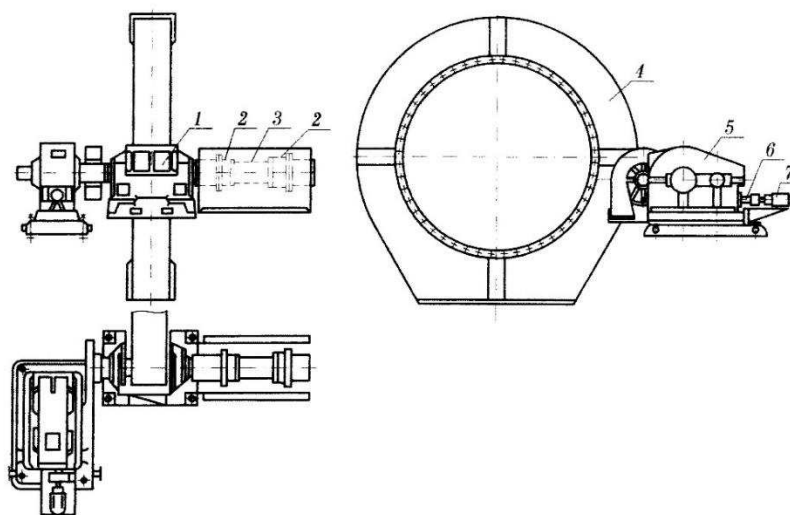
Привод мельницы МШРГУ–4500х6000
